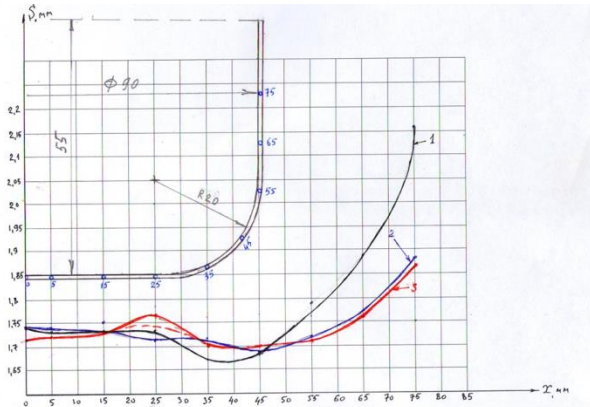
Изменения толщины стенки цилиндрической детали вдоль образующей после вытяжки
